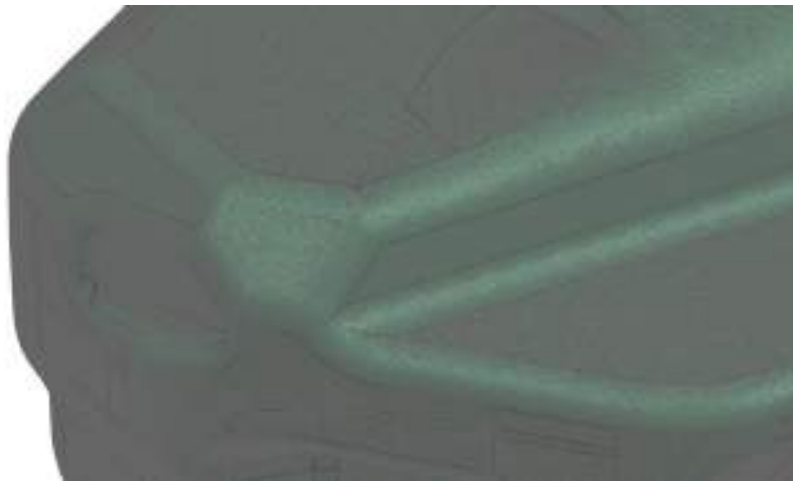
Звичайно-елементна сітка на корпусі паливного бака
